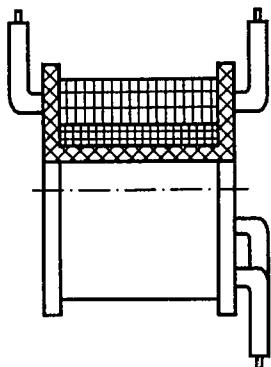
Зображення на кресленику багатошарової катушки
